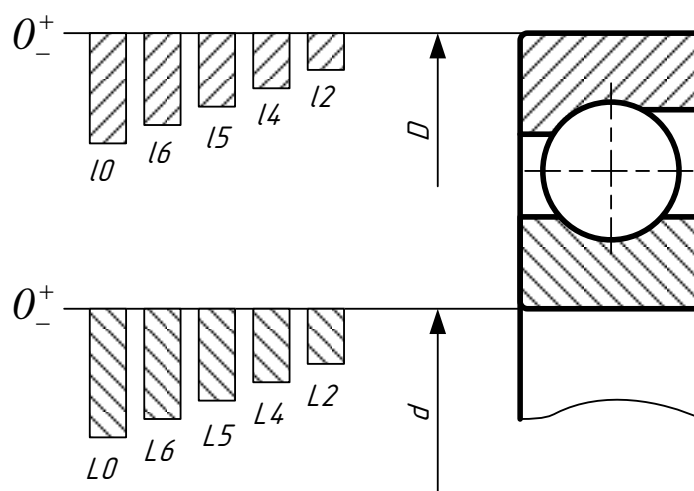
Схема расположения полей допусков на наружный диаметр и диаметр отверстия подшипников по классам точности
